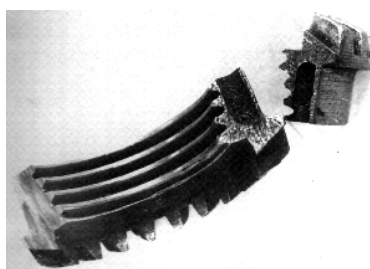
Разрушение шестерни редуктора из-за ослабления ее сечения засверловкой
